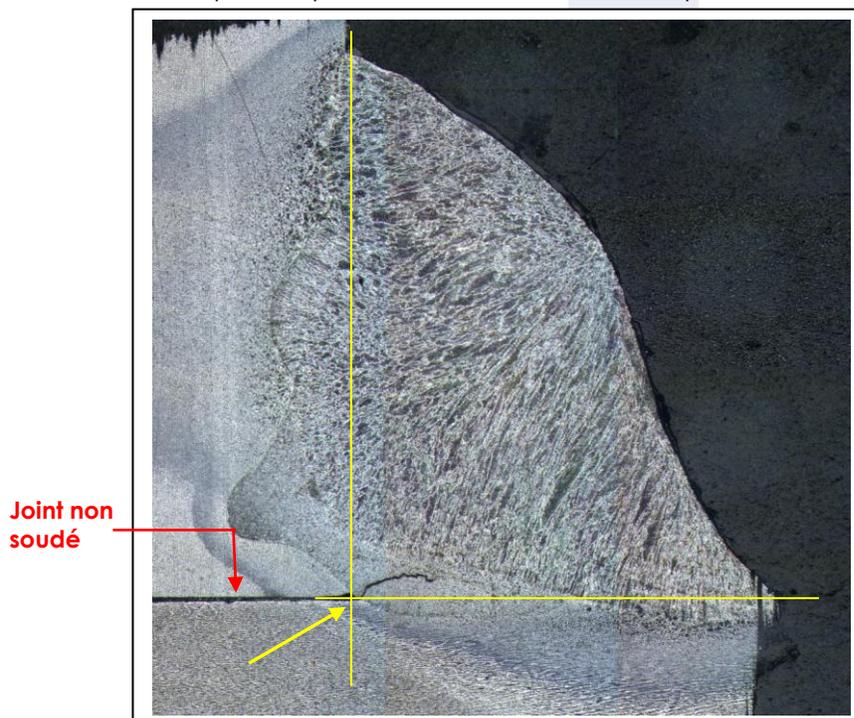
Fissure à la racine du cordon de soudure 1GE - surface ext.
